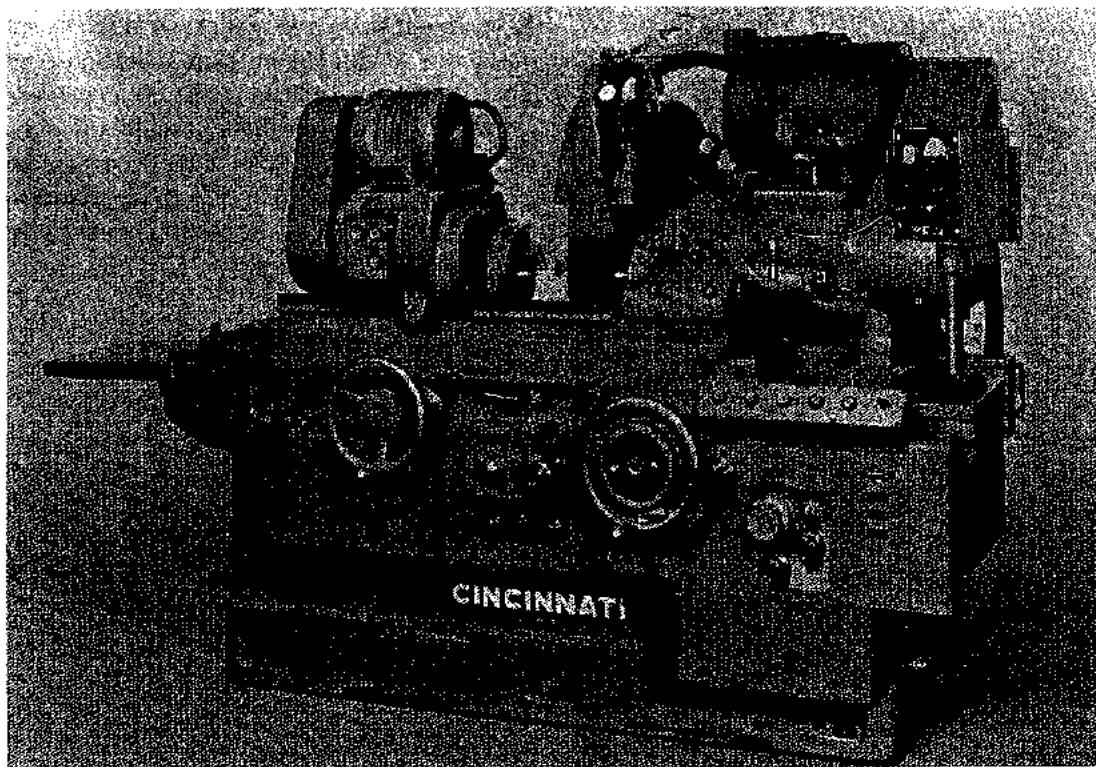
Rectificadora cilíndrica corriente, hidráulica (Cincinnati Milling Machine Co.)
